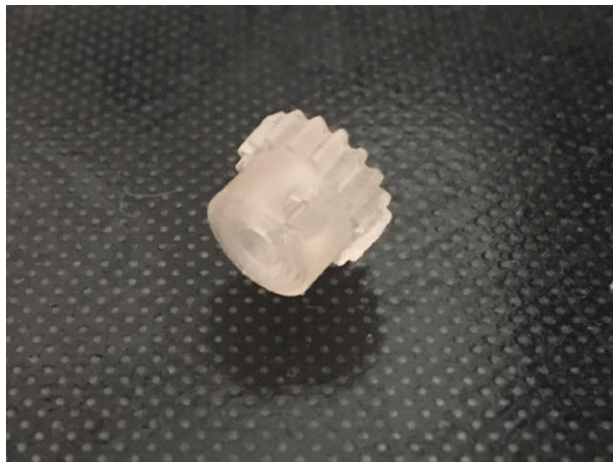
Rueda dentada fabricada mediante tecnología FDM. Fuente propia.
